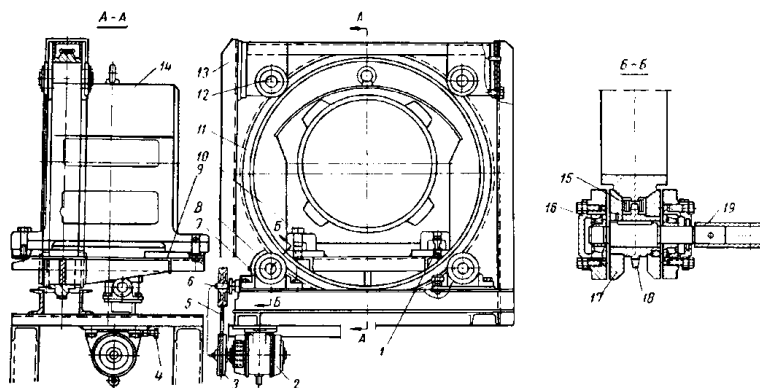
Кантователь для обмотки статоров двигателей 8 – 9 габаритов.
